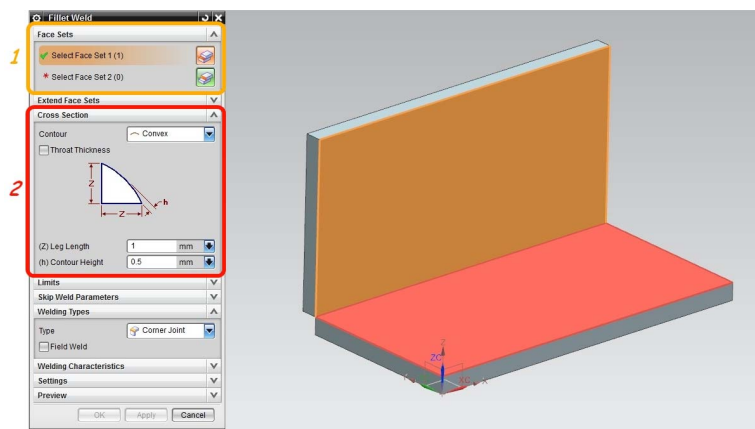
Выбор места сварки и задание параметров углового шва
